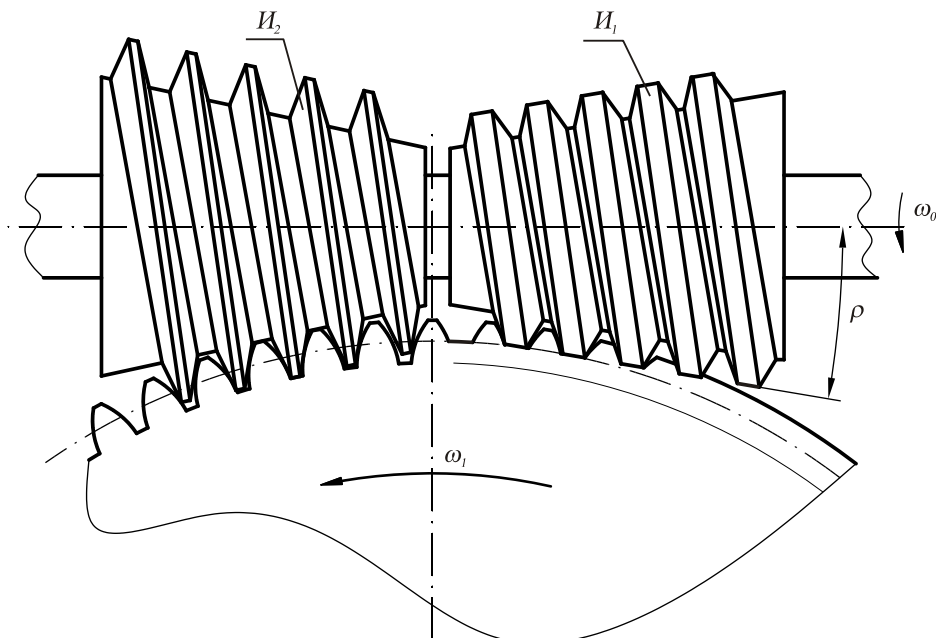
Схема формообразования двумя коническими червячными фрезами цилиндрических зубчатых колес.
